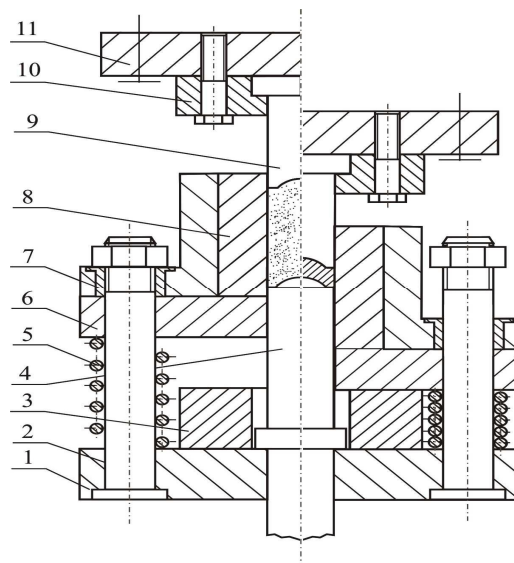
Схема штампа для виготовлення пресовки з компенсатором: 1 – нижня плита; 2 – стовпчик; 3 – упор; 4 – виштовхувач; 5 – пружина; 6 – плита матриці; 7 – втулка; 8 – матриця; 9 – пуансон; 10 – фланець; 11 – верхня плита
